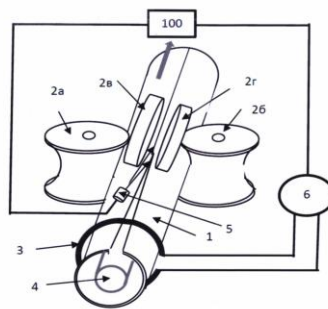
Схема реализации предлагаемого способа и устройства управления процессом контактной стыковой сварки стальных электросварных труб.
